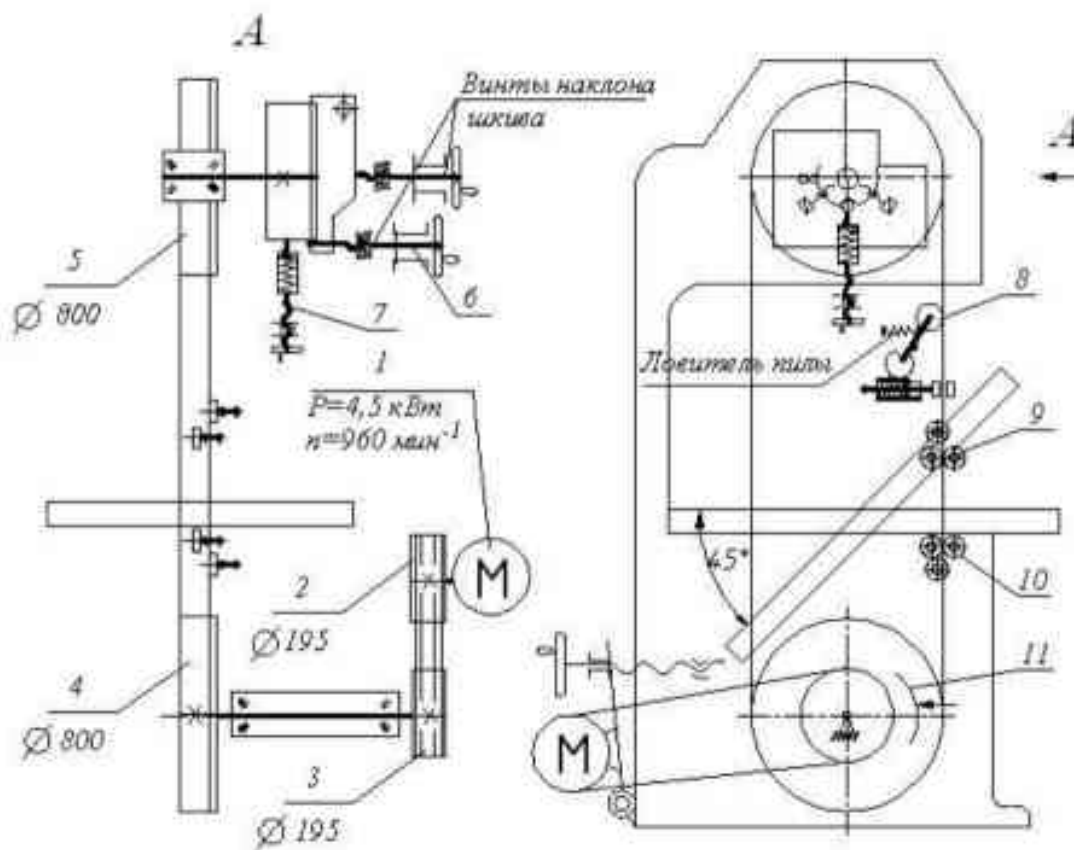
Кинематическая схема ленточнопильного станка ЛС-80-5
